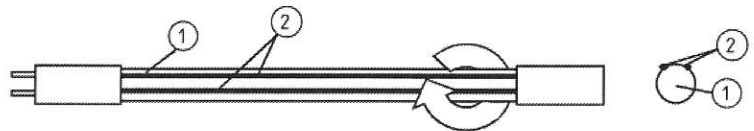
Installationstegning af UV 60 S – 200 S lampe
